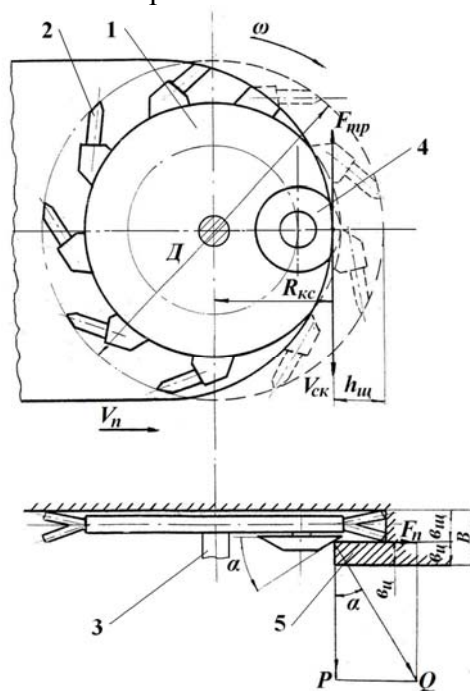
Расчетная схема РО, состоящего из режущего диска, прорезающего опережающую щель, и клинового устройства, скалывающего целик: 1 – режущий диск; 2 – резцы; 3 – приводной вал; 4 – коническая шарошка; 5 – целик
